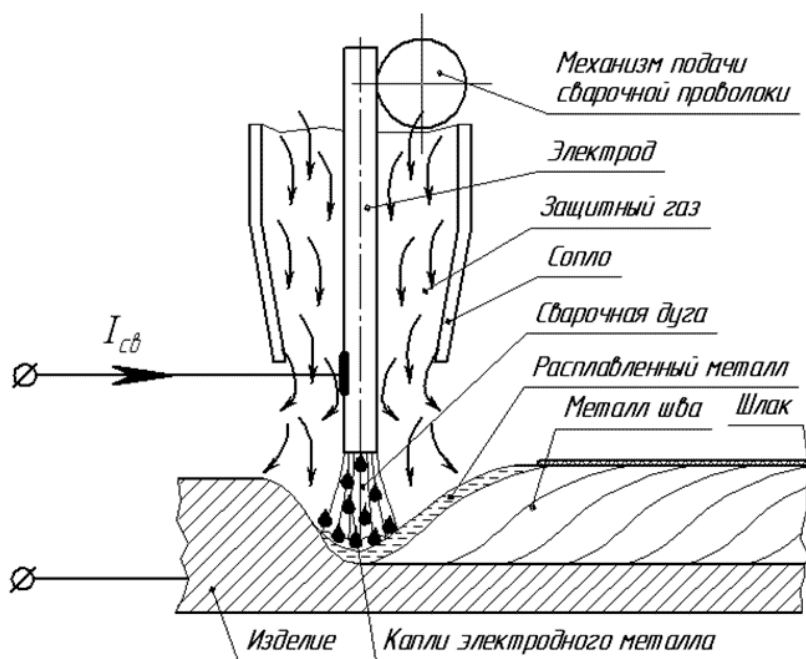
Схема сварки в среде защитных газов
